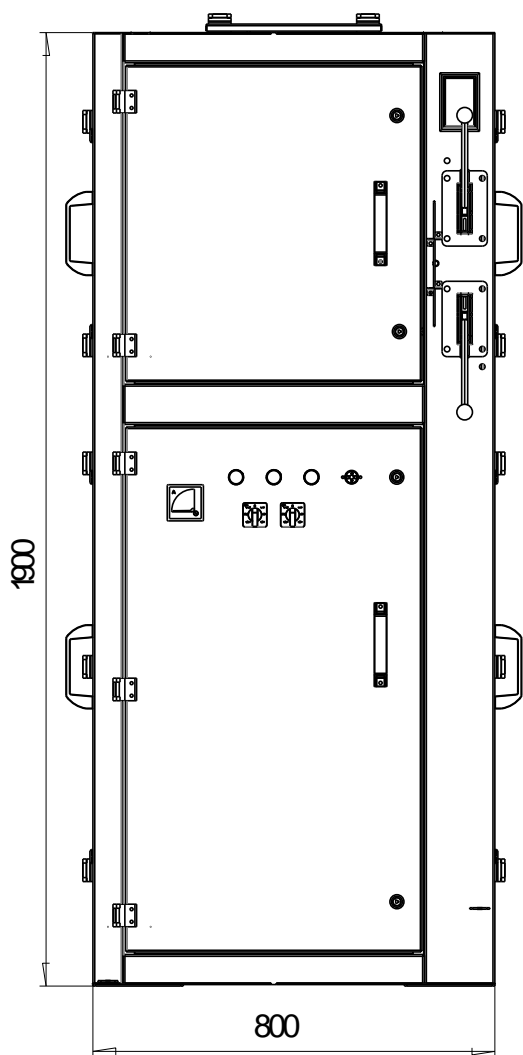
Габаритные размеры КРУ-2КВЭ-6
